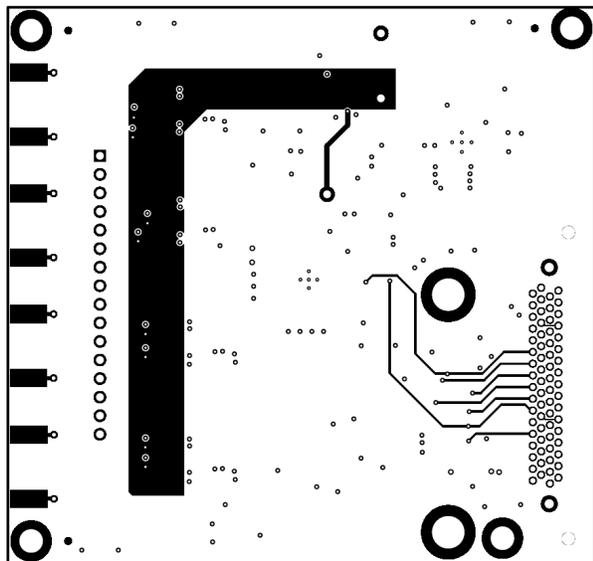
ADS8332EVMV2 PCB 第 4 层：底层
